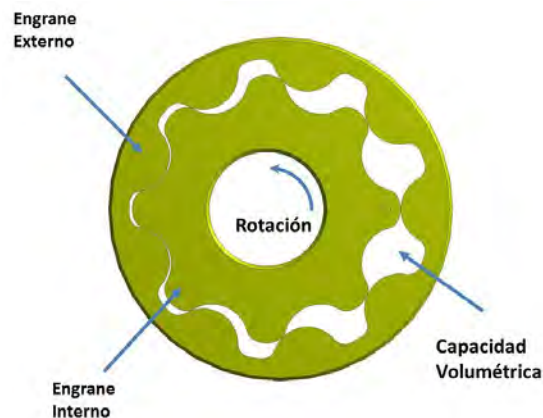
Conjunto de engrane externo e interno del sistema GERotor
